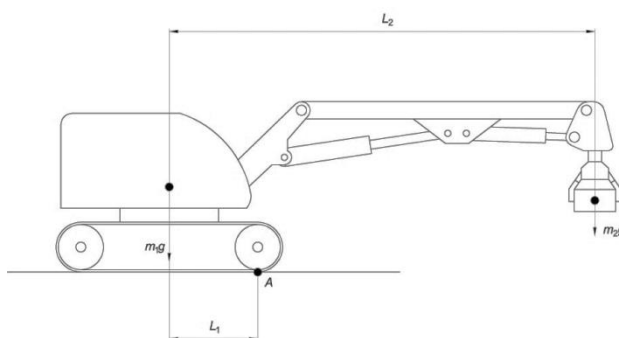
Схема расчета робота на устойчивость без аутригеров
